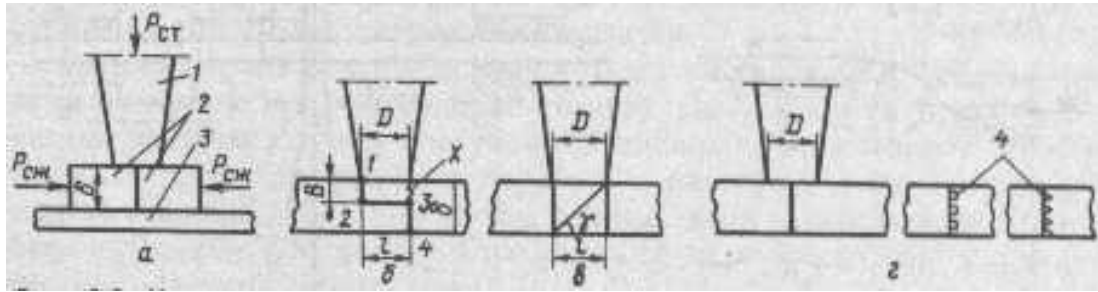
Конструкции стыковых соединений при сварке с дополнительным усилием сжатия  $P_{сж}$ , перпендикулярным  $P_{ст}$ : а - "плоский стык"; б - "замковое соединение"; в - соединение "в ус", г - соединение с концентраторами напряжений в зоне сварки, 1 - сварочный инструмент-волновод; 2 - свариваемые детали; 3 - опора; 4 - виды концентраторов напряжений; 5 - толщина изделия; в - толщина полки замкового соединения; D - ширина свариваемого участка, равная диаметру волновода; X - участок опасного сечения при сварке
